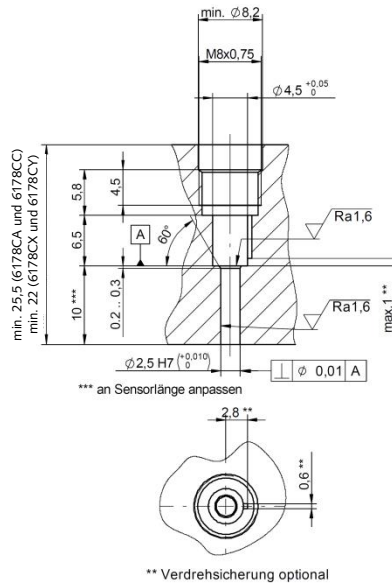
Montagebohrung für Einbau mit Montagemutter.
